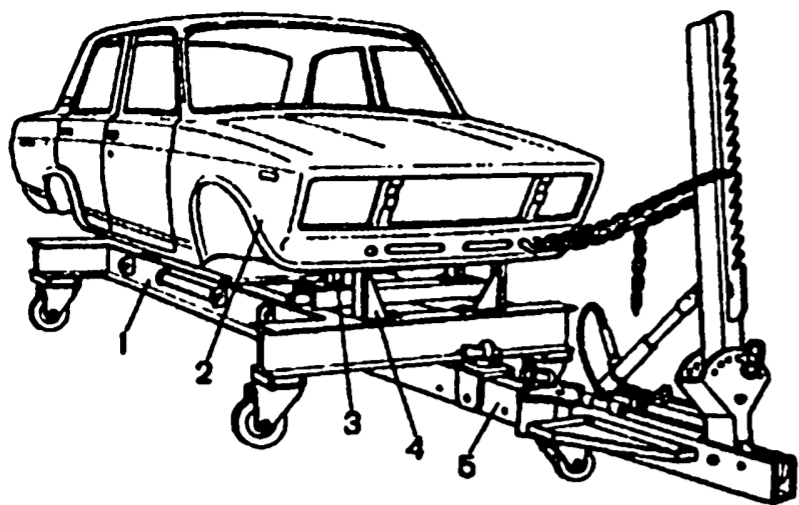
Установка для ремонта и контроля кузова с приспособлением для правки: 1 - рама установки; 2 - кузов автомобиля; 3 - кронштейн крепления поперечины передней подвески; 4 - кронштейн крепления стабилизатора поперечной устойчивости; 5 - приспособление для правки со стрелой и гидравлическим устройством
